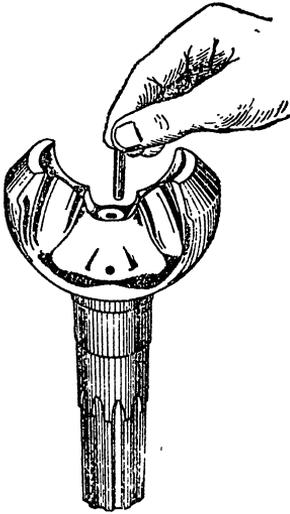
Установка стопорного пальца в отверстие ведомой вилки кардана
